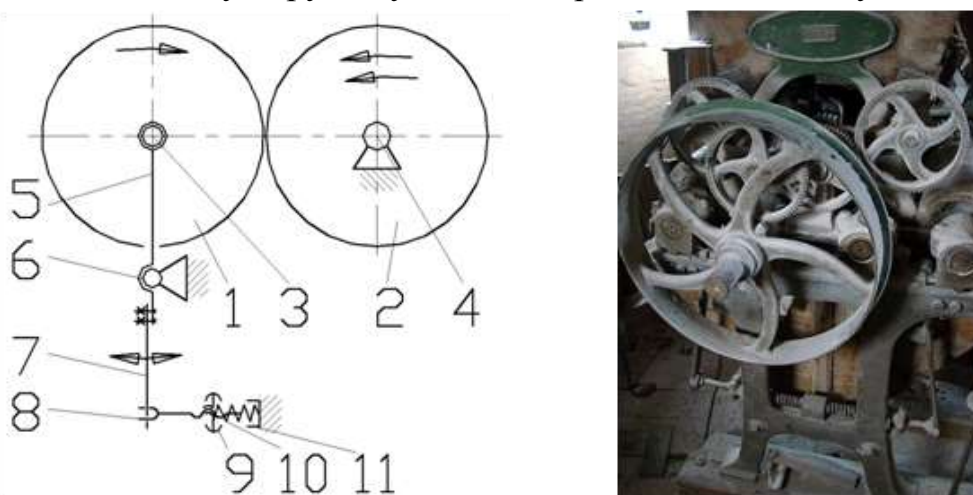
Схема (а) і загальний вид (б) вальцьового верстата.
